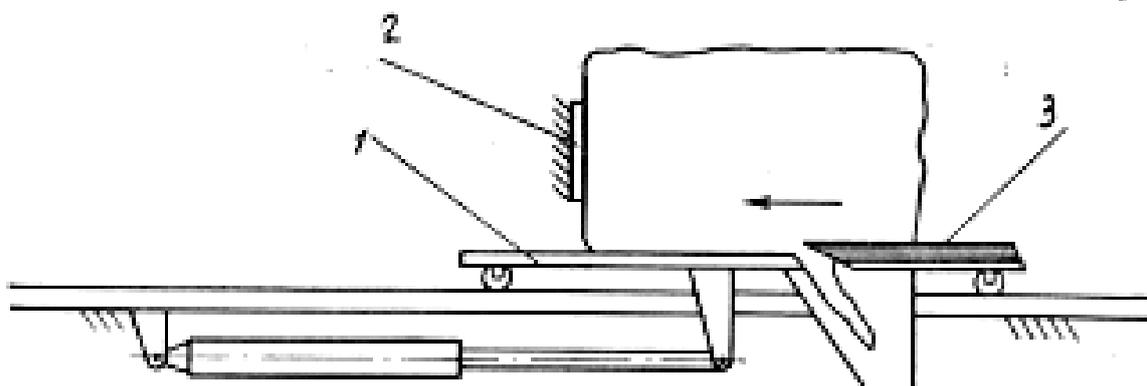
Машина для снятия корок: 1 – подвижной стол; 2 – неподвижный упор; 3 – нож
